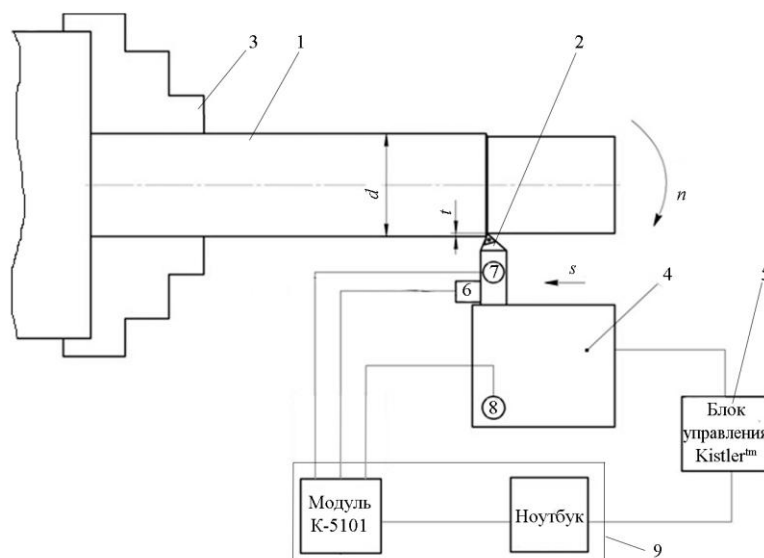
Принципиальная схема УМР для проведения эксперимента: 1 – образец горной породы; 2 – сборный инструмент; 3 – трехлапчатый патрон; 4 – резцедержатель; 5 – регистрирующее силовое устройства марки Kistlertm; 6–8 – акселерометры; 9 – мобильный комплекс для оперативной диагностики элементов технологической системы
